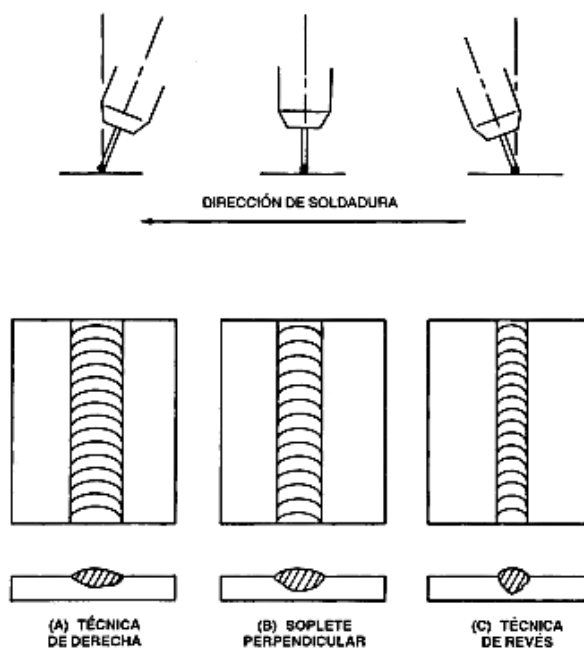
8 Efecto de la posición del electrodo y de la técnica de soldadura (16).
